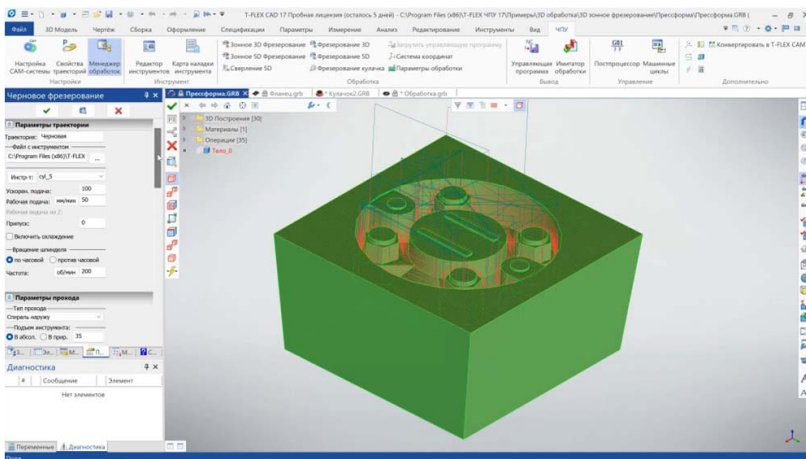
Редактор постпроцессоров обработки массива внутренней поверхности [9]
